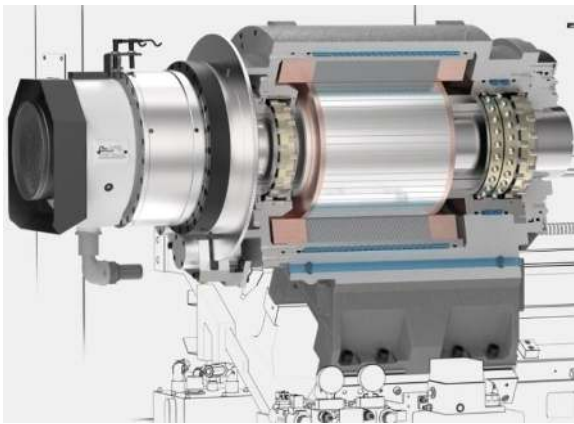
Корпус мотор-шпинделя станка TD Z2200 (Италия)
